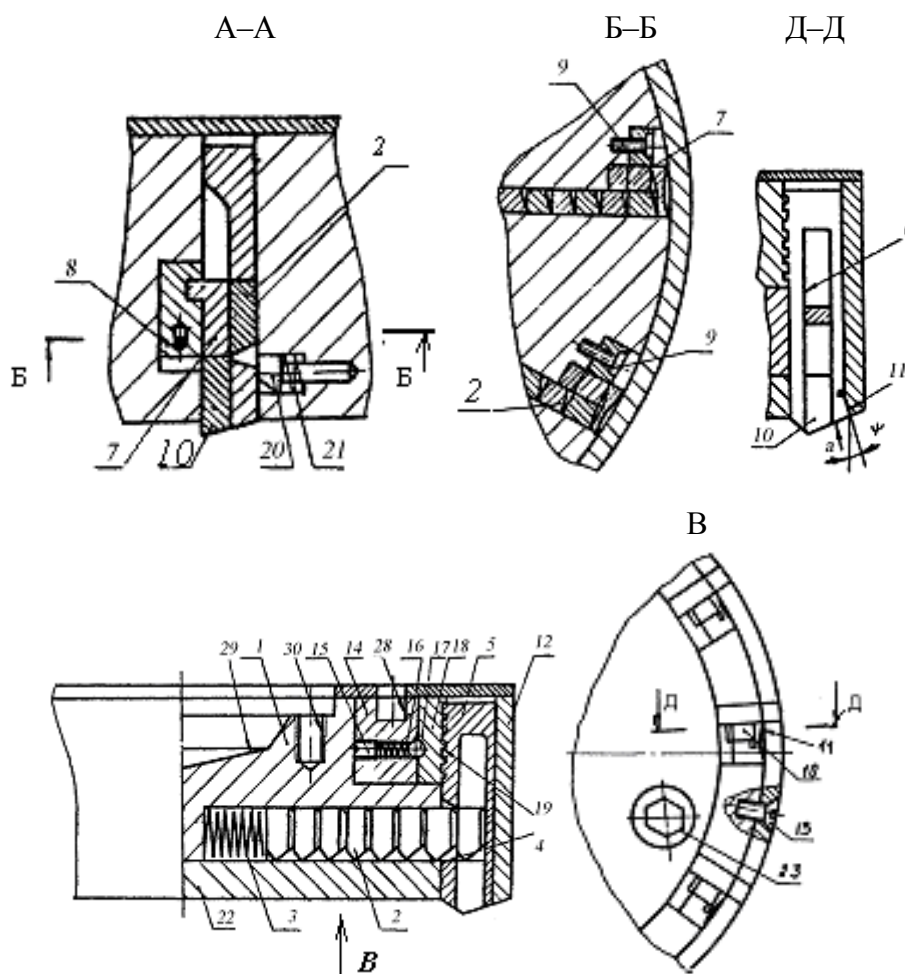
Эскиз инструмента с механизмом замены режущих пластин
